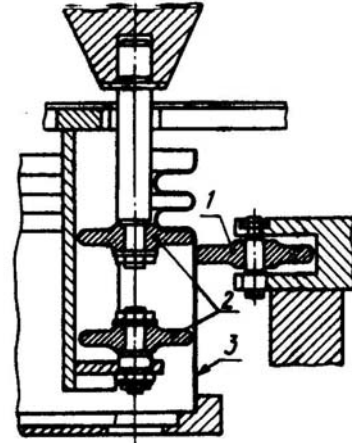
Приспособление для изготовления гибких элементов на карусельном станке
